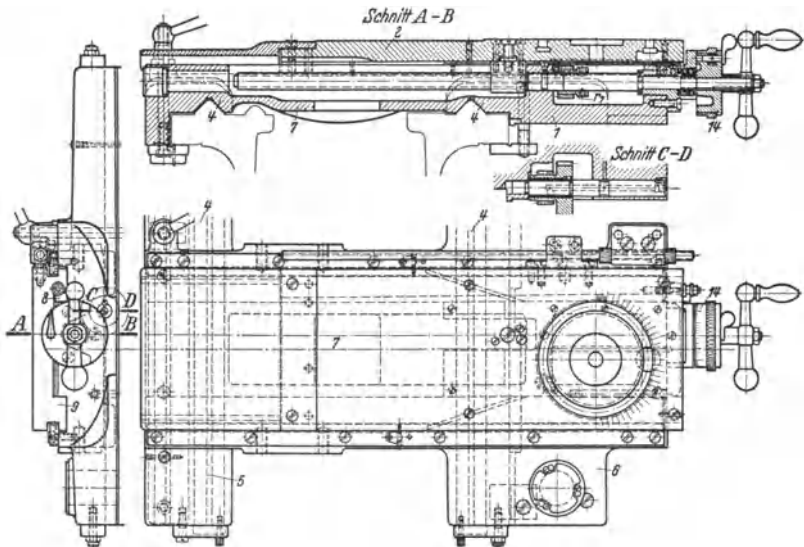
Bett- und Planschlitten (Supportschlitten), (Loewe, Berlin).
